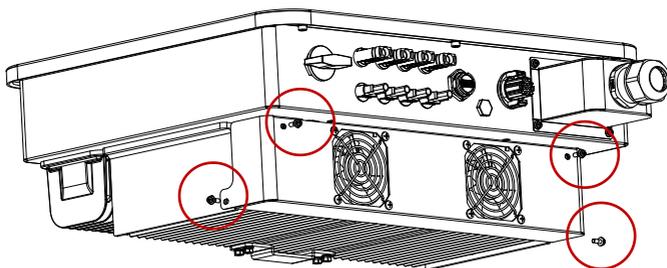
Entfernen Sie die vier Schrauben von der Lüftergrundplatte.
